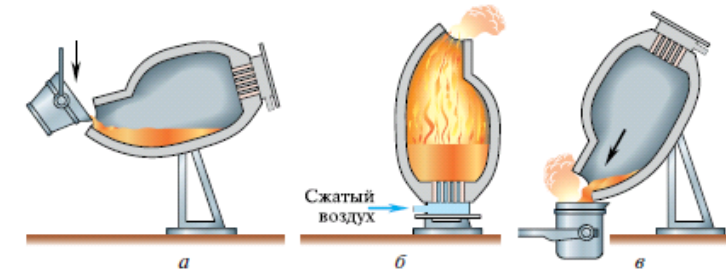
Процесс выплавки стали в конверторной печи:
